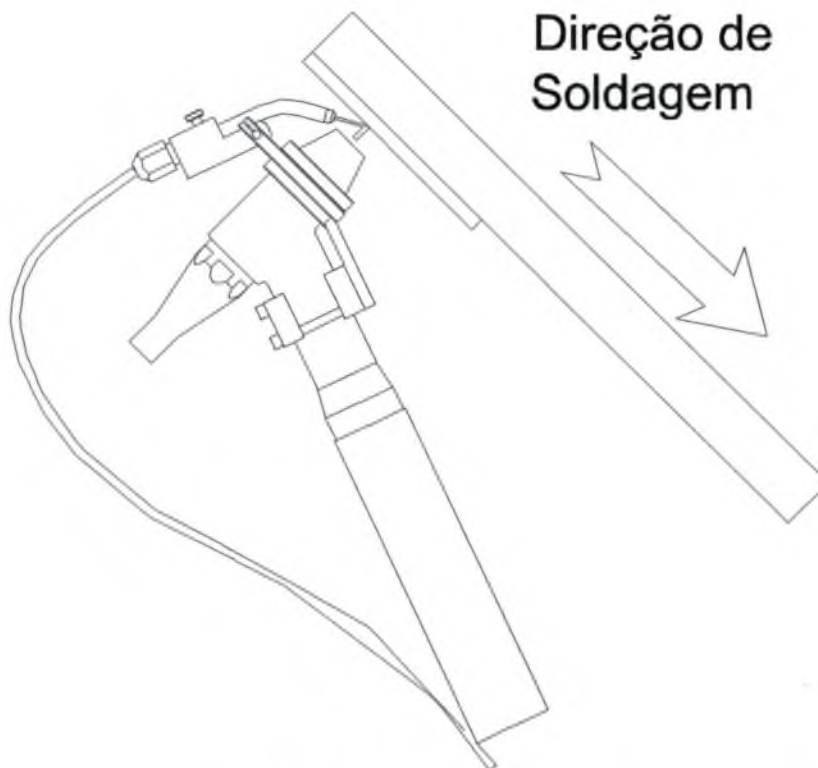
Soldagem na Posição Sobrecabeça
